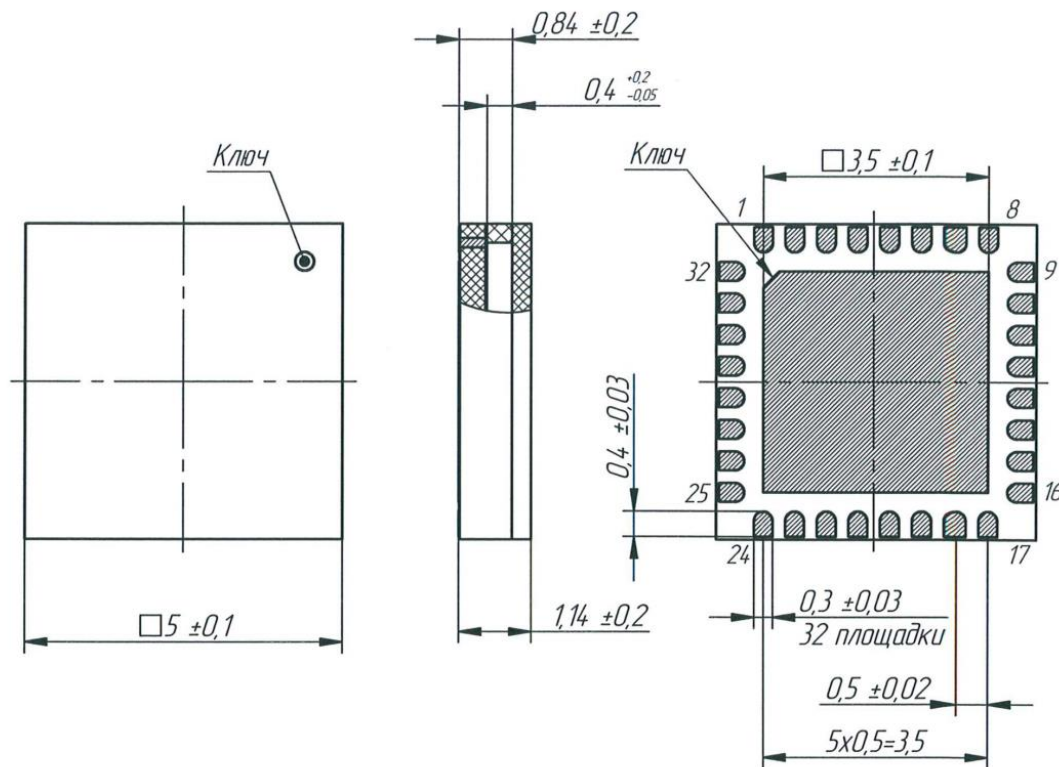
Габаритный чертёж корпуса IPA0027-Q
